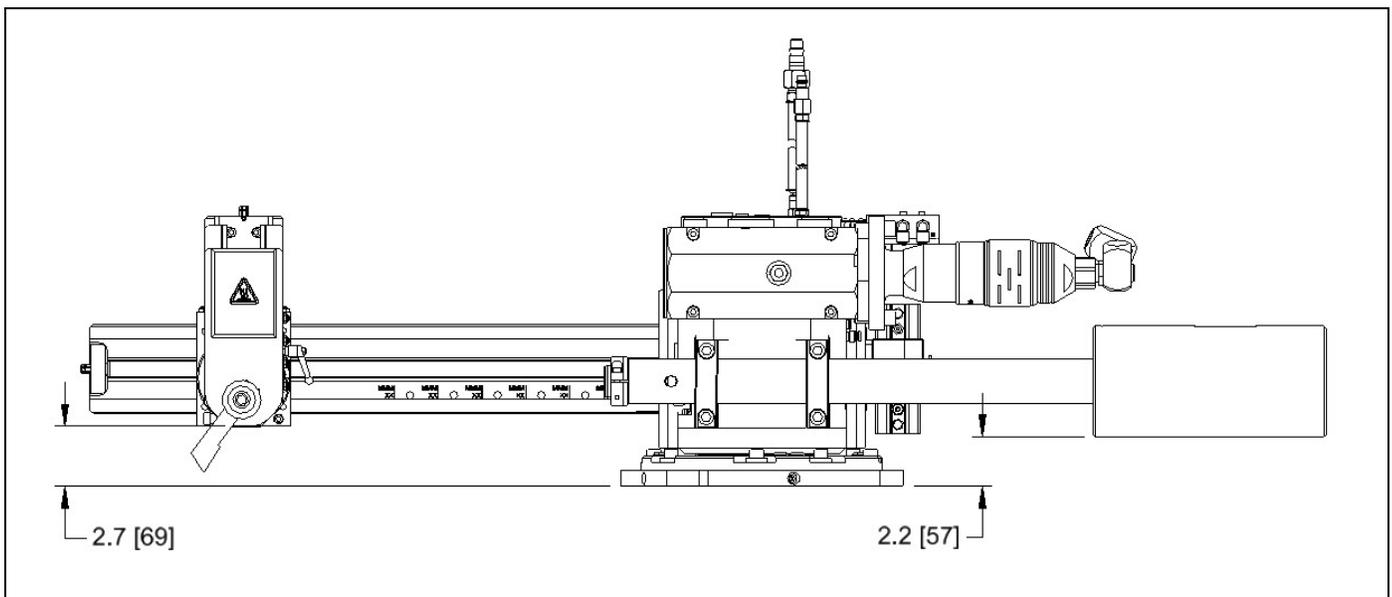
DIMENSIONES DEL ENSAMBLAJE DE SOPORTE EN SUPERFICIE FF6300
